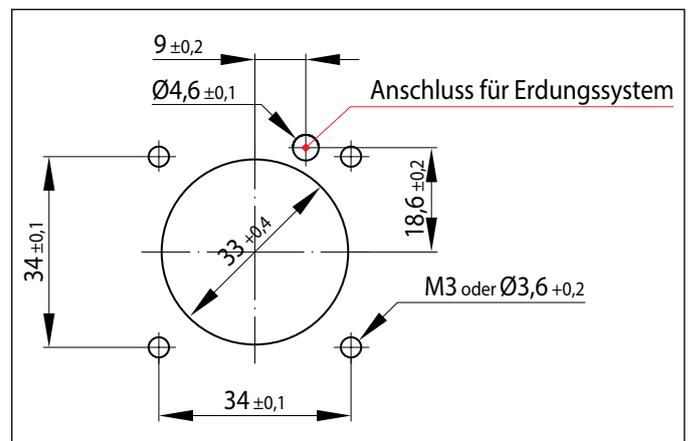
Maße und Anordnung der Montagebohrungen/Gewinde für Stecker mit Flansch GA SF 1SC (Maße in mm)
